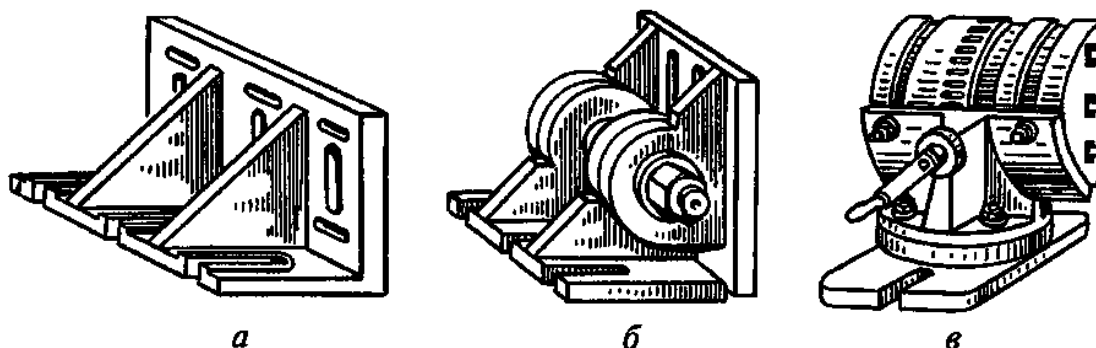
Угловые плиты для закрепления заготовок на столе фрезерного станка
